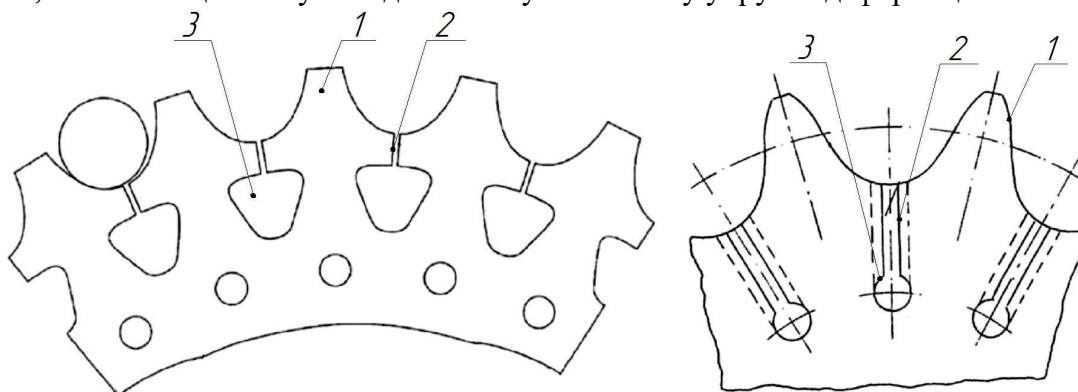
Звездочки с консольными зубьями, образованными радиальными прорезями: 1 – зуб звездочки; 2 – радиальная прорезь; 3 – отверстие
